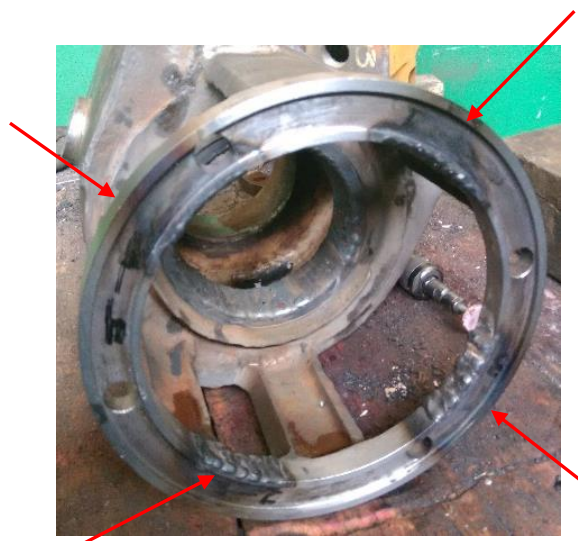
Zonas con presencia de rechupes, reparadas con soldadura.
